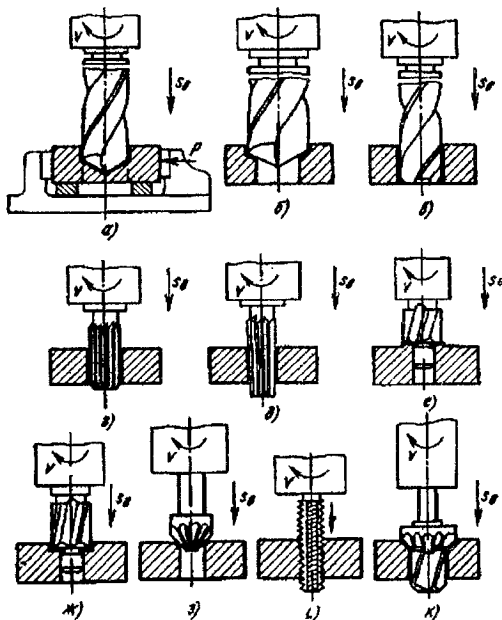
Деякі схеми обробки отворів мірними інструментами:
